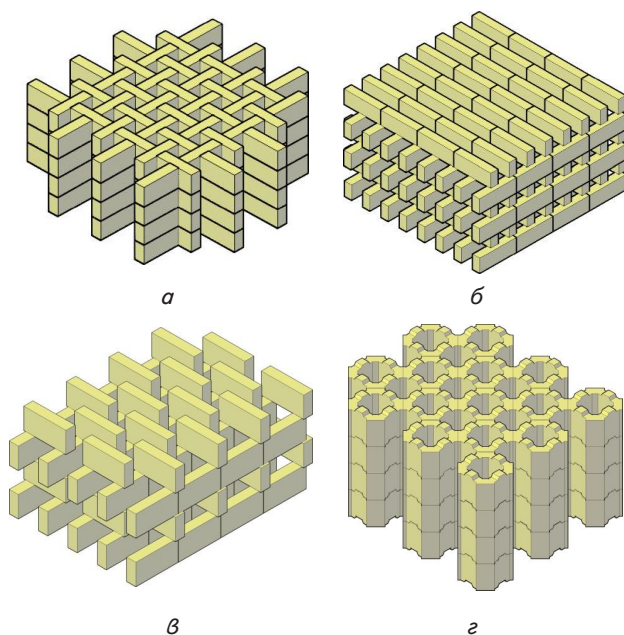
Основные типы насадок регенераторов стекловаренных печей: а – насадка Каупера; б – насадка Сименса без смещения каналов; в – насадка Лихте; г – корзиночная насадка из формовых элементов
